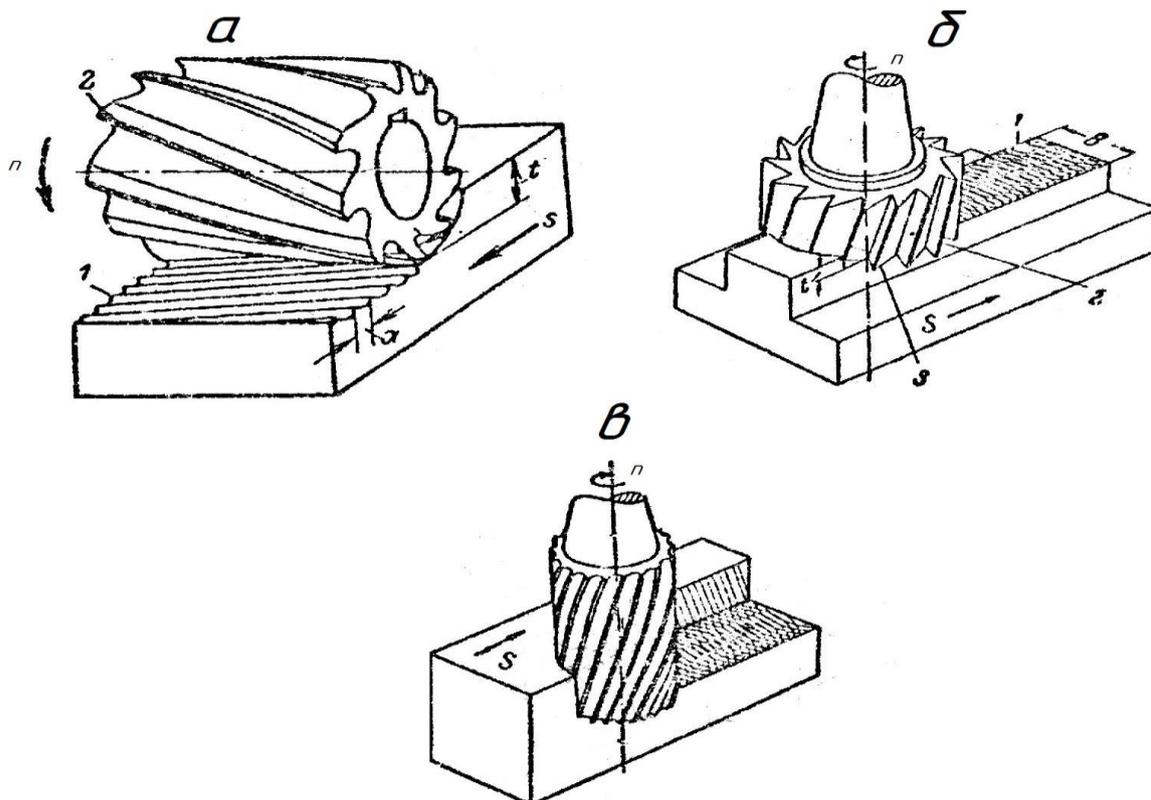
Виды фрезерования: а-цилиндрическое; б-торцовое; в-комбинированное
